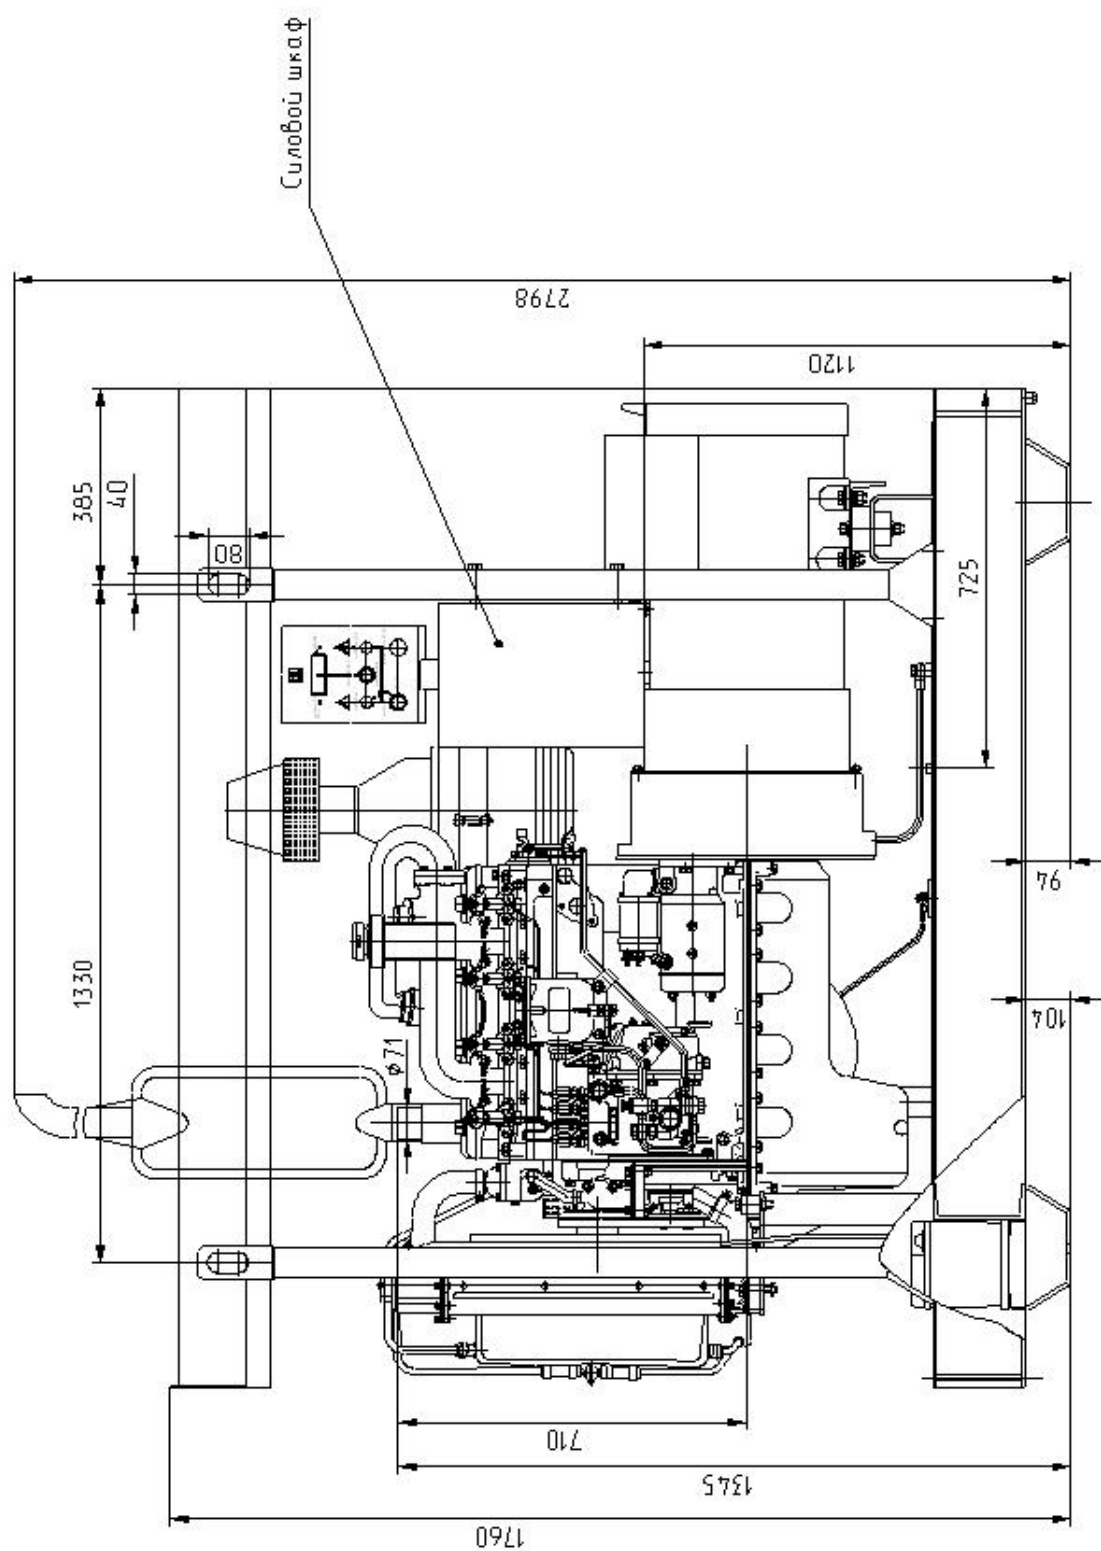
Монтажный чертёж установки ДГ-60 (вид сбоку).
